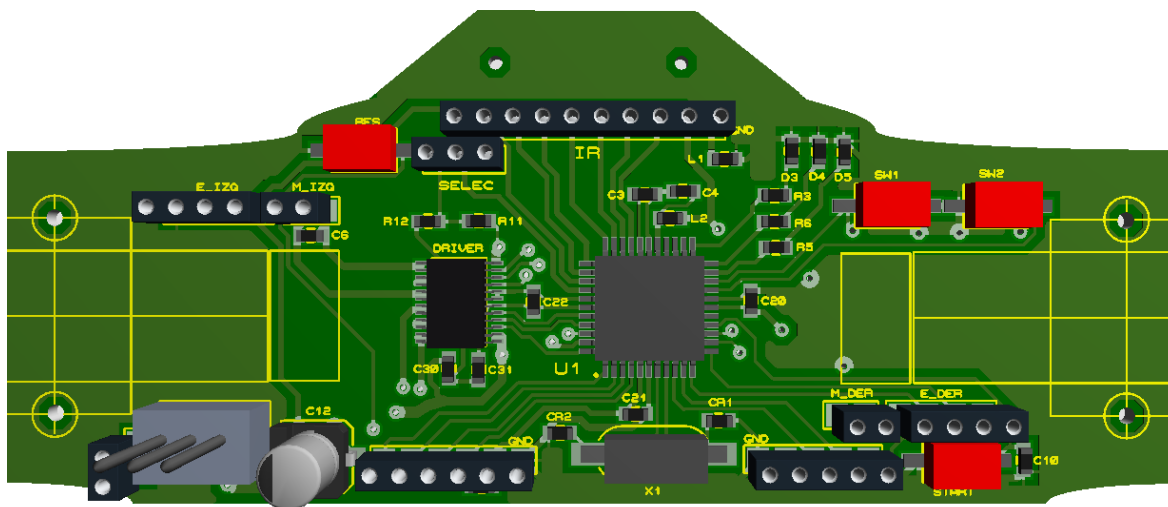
Tarjeta de control robot seguidor de línea, vista superior.
